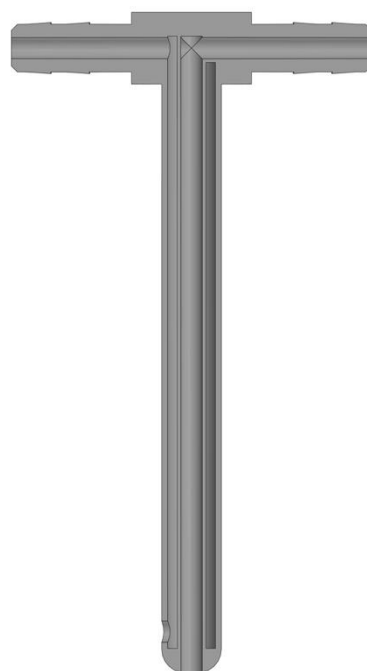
Трубка Пито-Прандтля со сферической поверхностью вокруг отверстия статического напора, образец III, разрез
